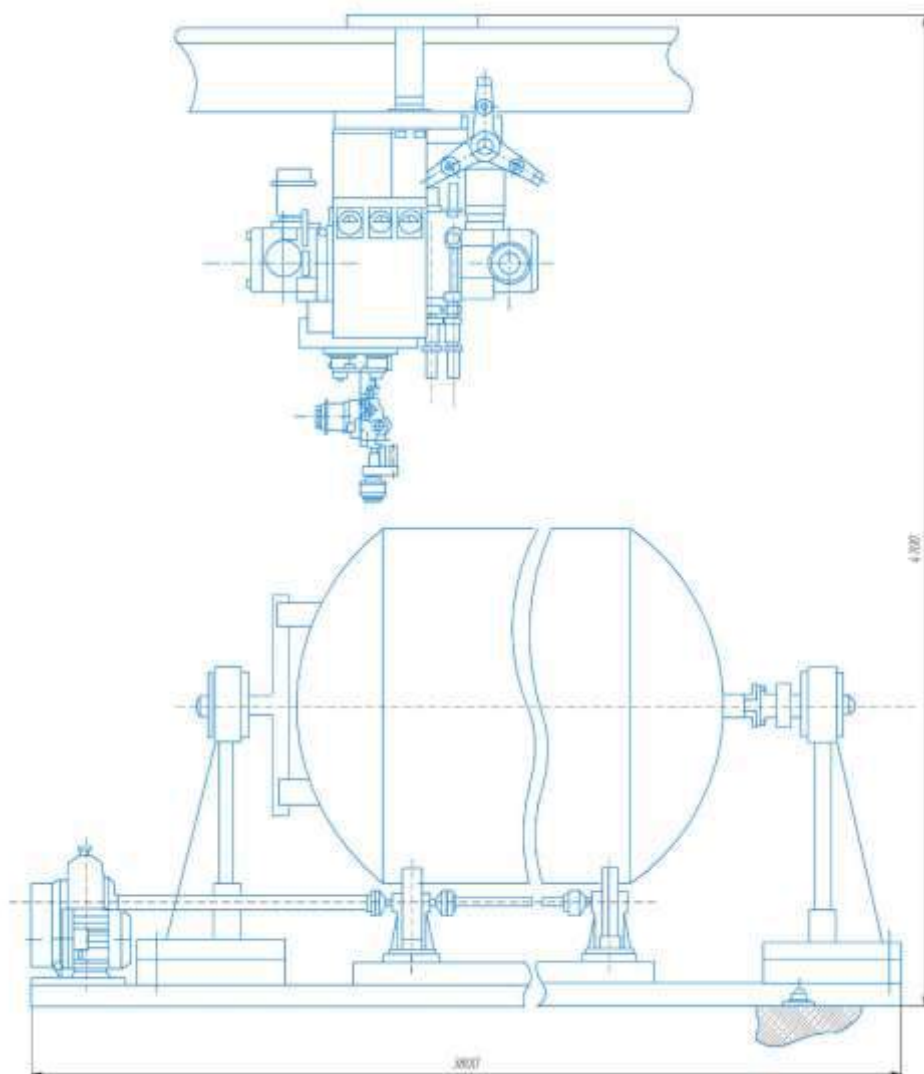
Загальний вигляд обладнання для зварювання
